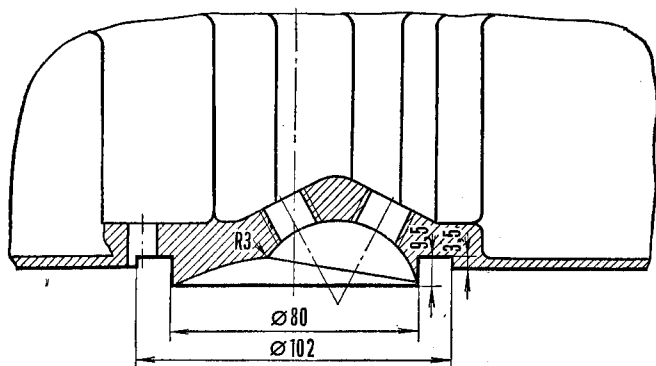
Переделка головки цилиндра для двигателя 320 см³
